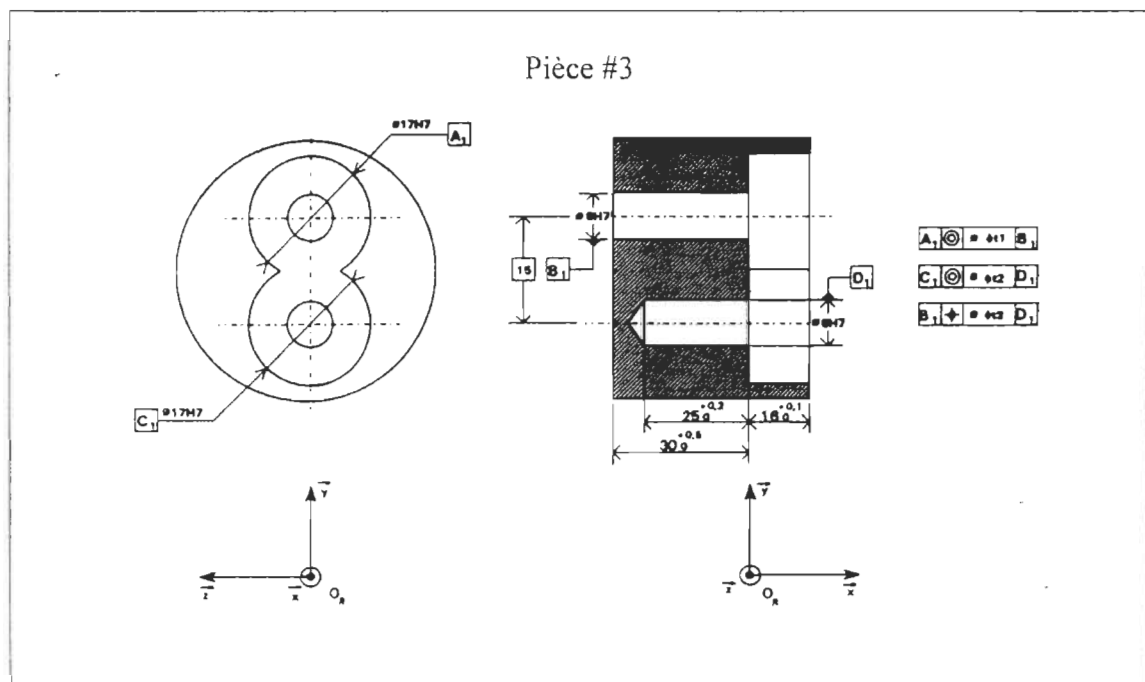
Mécanisme de la pompe à engrenage : corps principal
